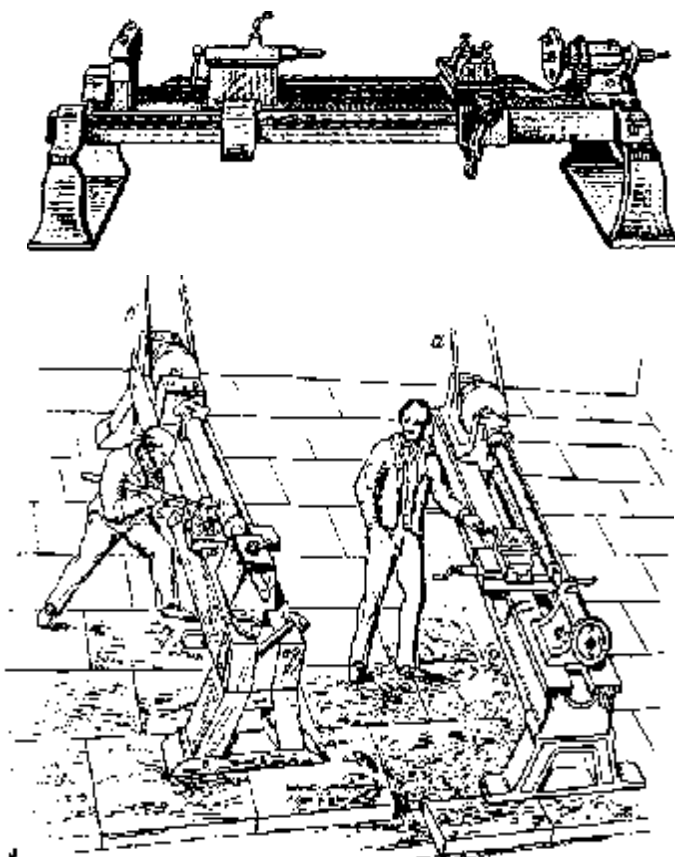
Первый токарный станок с суппортом Г. Модсли (сверху) и рекламный плакат автоматического суппорта
